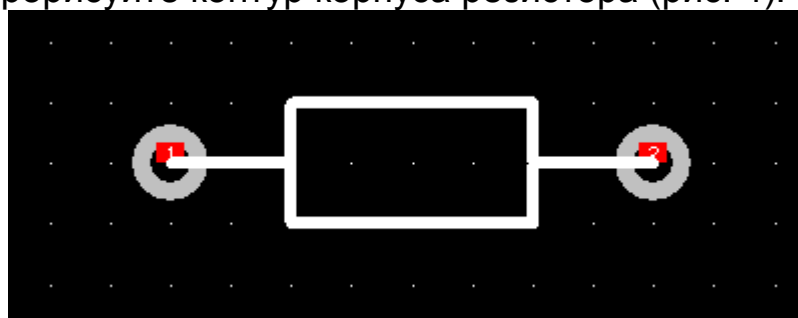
Корпус резистора (Grid=1.25mm)
